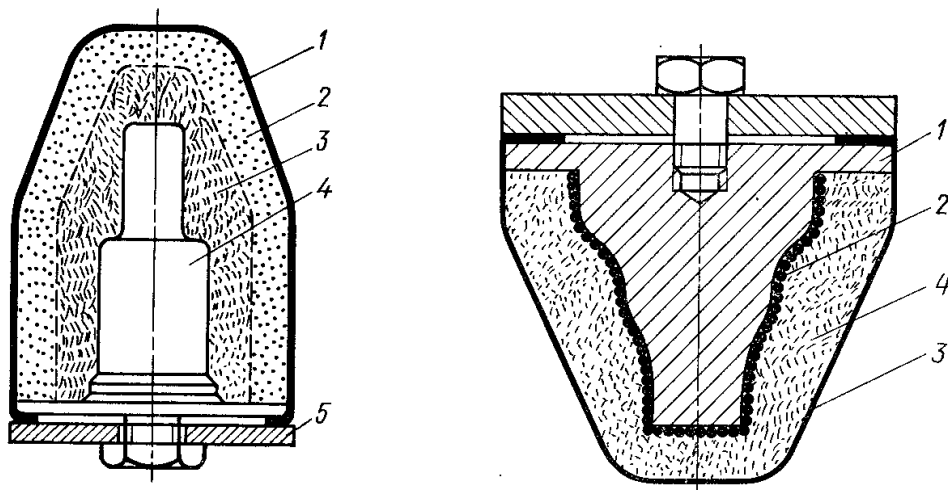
Схема отримання 1 - еластична оболонка; 2, 3 – металічний армованого кокілю порошок; 4 - модель; 5 - пластина
